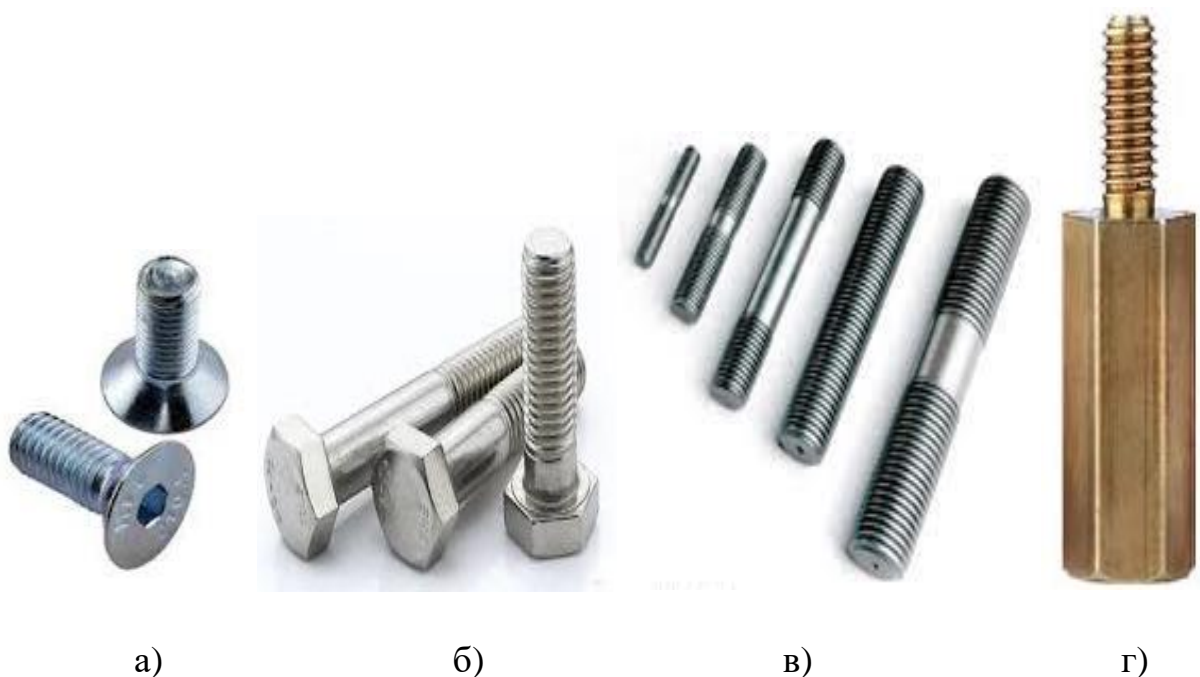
Деталі різьбові кріпильні осьові: а – гвинти; б – болти;
